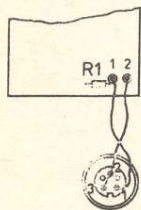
Deska odpínání 3AK 052 79 - strana spojů
